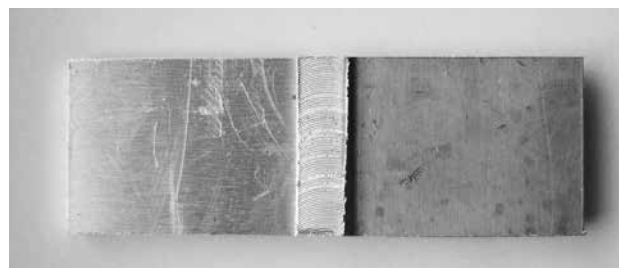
Образец сварного шва соединения АМг5 – М1
